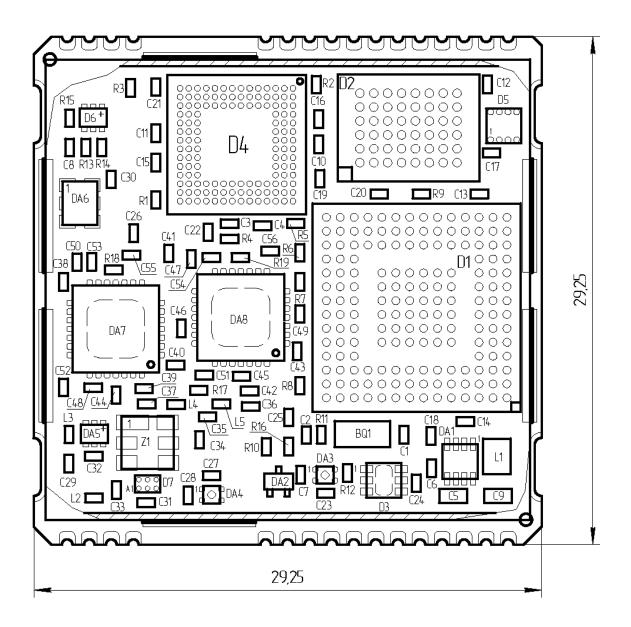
Габаритные размеры МНП-М7 для исполнения ЦВИЯ.468157.113 / Figure 4 – Overall dimensions of MNP-M7 for CVIA.468157.113 modification
